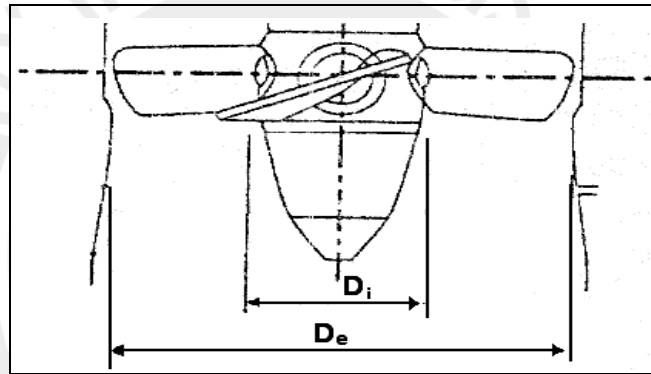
Dimensiones principales de la turbina Kaplan, según F. Schweiger [8].
